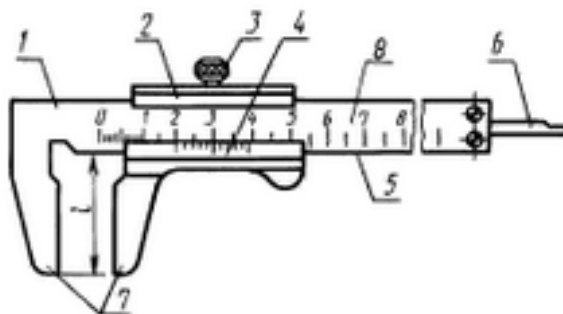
Штангенциркуль односторонний с глубиномером с измерительными поверхностями из твердых сплавов
